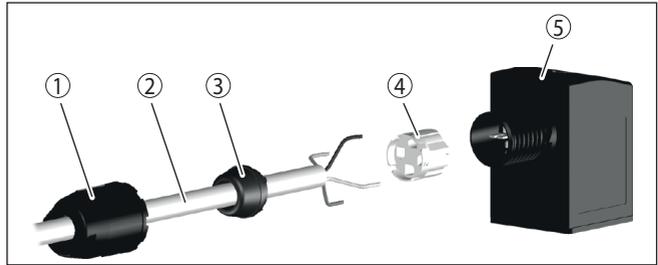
Conexión enchufe de válvula ISO 4400 con técnica de desplazamiento de aislamiento
